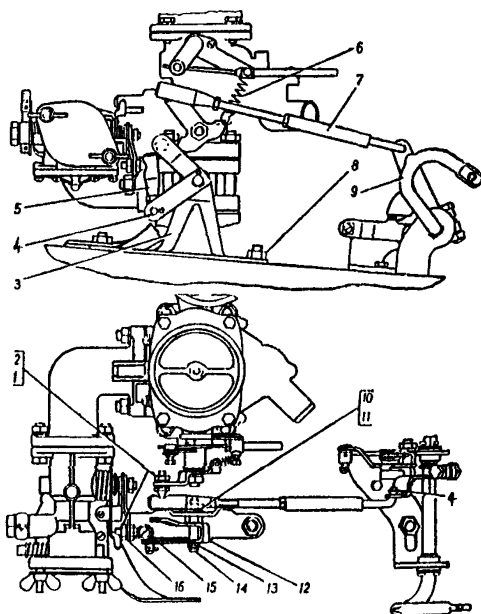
Установка привода акселератора двигателя ГАЗ-53-07
